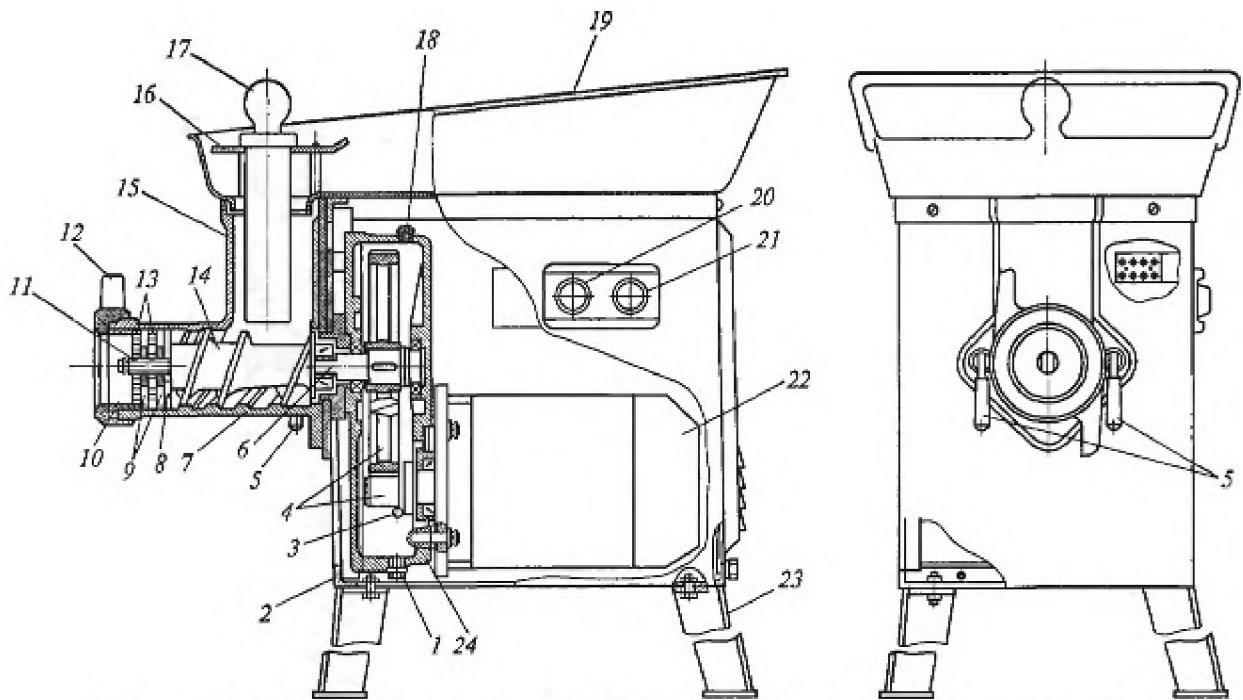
М'ясорубка МИМ-300: 1 – отвір зливний; 2 – рама; 3 – кришка редуктора; 4 – редуктор циліндричний; 5 – затискач; 6 – втулка; 7 – корпус; 8 – решітка підрізна; 9 – ножі, що обертаються; 10 – кільце упорне; 11 – палець; 12 – гайка затискна; 13 – решітки ножові; 14 – шнек; 15 – горловина; 16 – запобіжник; 17 – штовхач; 18 – отвір для заливання мастила; 19 – чаша; 20, 21 – кнопки «Стоп» та «Пуск»; 22 – електродвигун; 23 – опора; 24 – корпус редуктора
